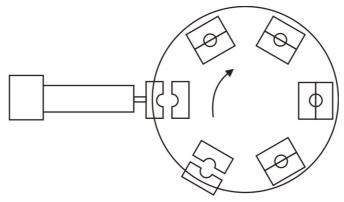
Máquina de extrusión-soplado continua tipo rotatorio.
